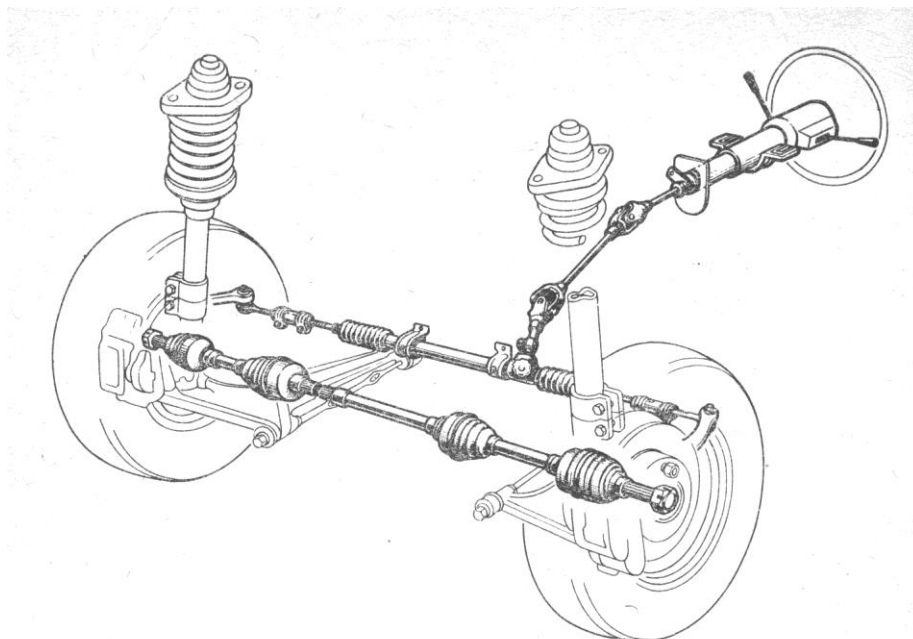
Привод передних колес легкового автомобиля с рулевым валом.
